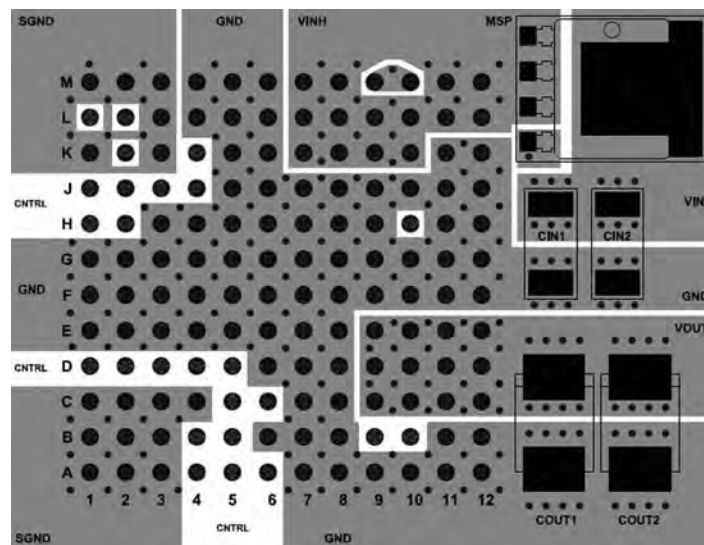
：推荐的 PCB 布局，图 46 所示电路。从封装的顶部观看 LTM4641。
